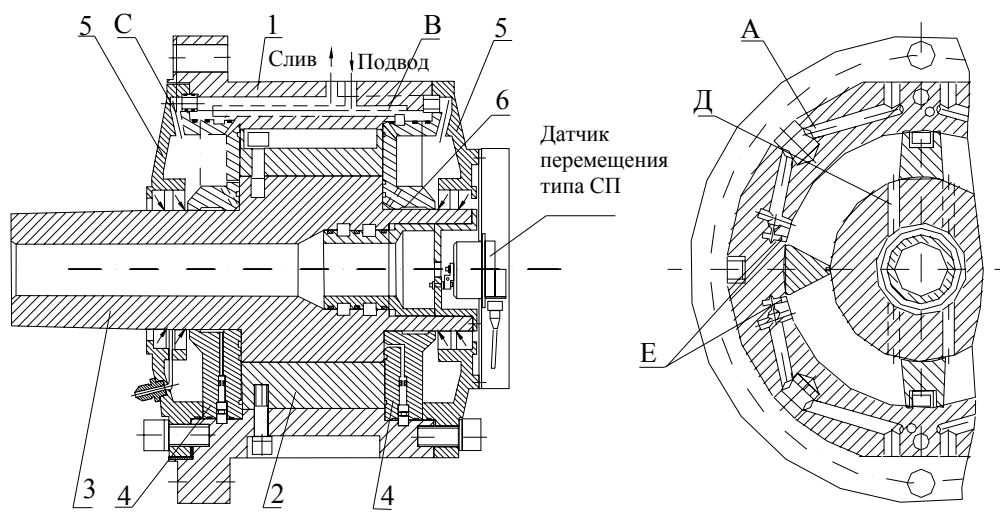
Конструктивная схема гидродвигателя типа НПМ
